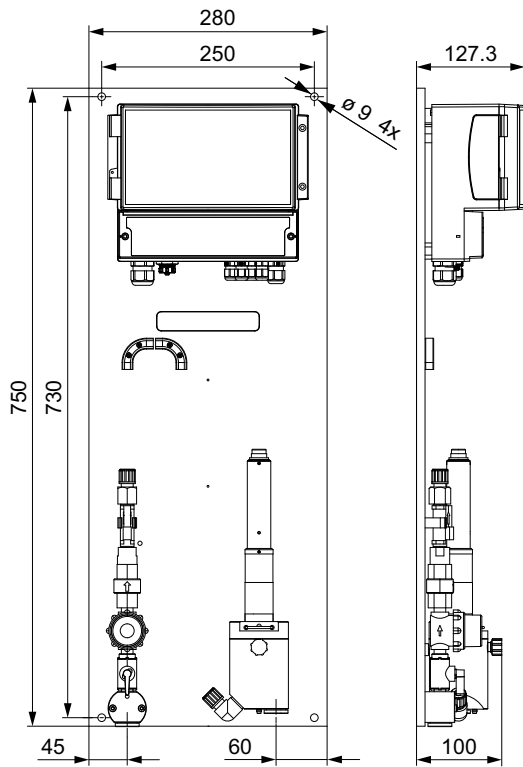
Abmessungen (in mm) des DID mit Durchflusszelle, Installationsausführung BF1 für einen Sensor
